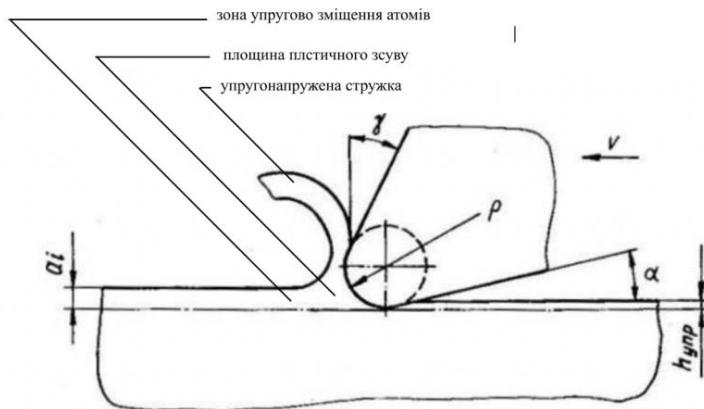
Схема врізання зуба фрези при швидкісному зубофрезеруванні
